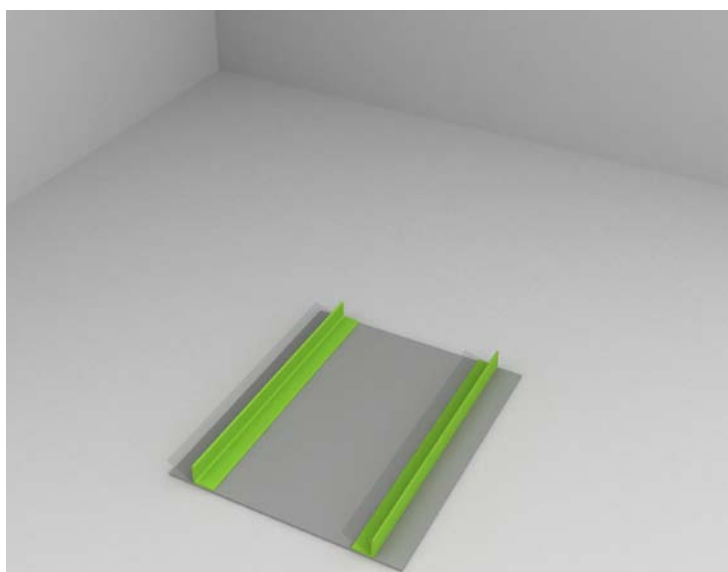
Montaj model instalație IIECON . Etapa 2. Corniere prindere.
